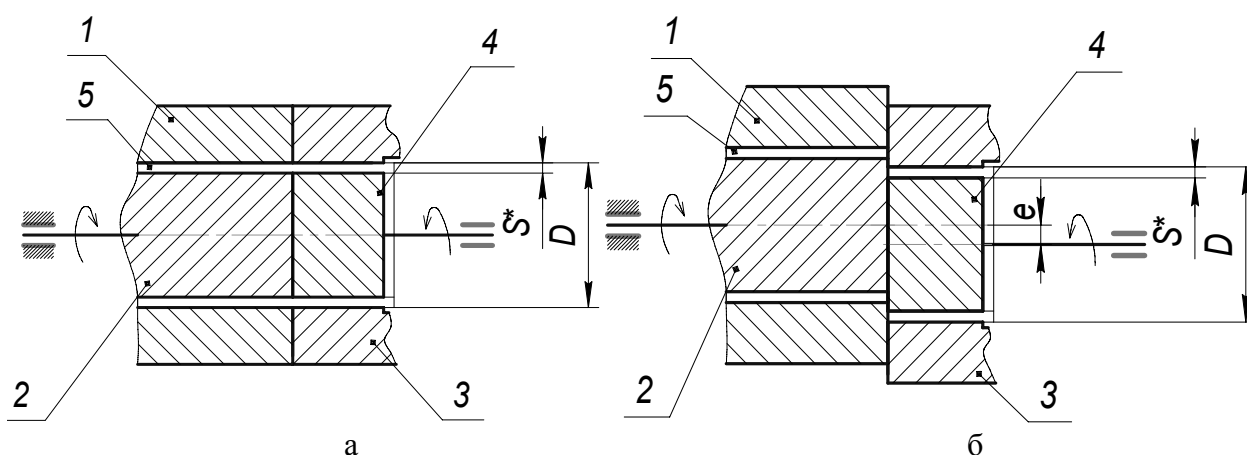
Схема устройства для резки труб одновременным сдвигом и кручением:
